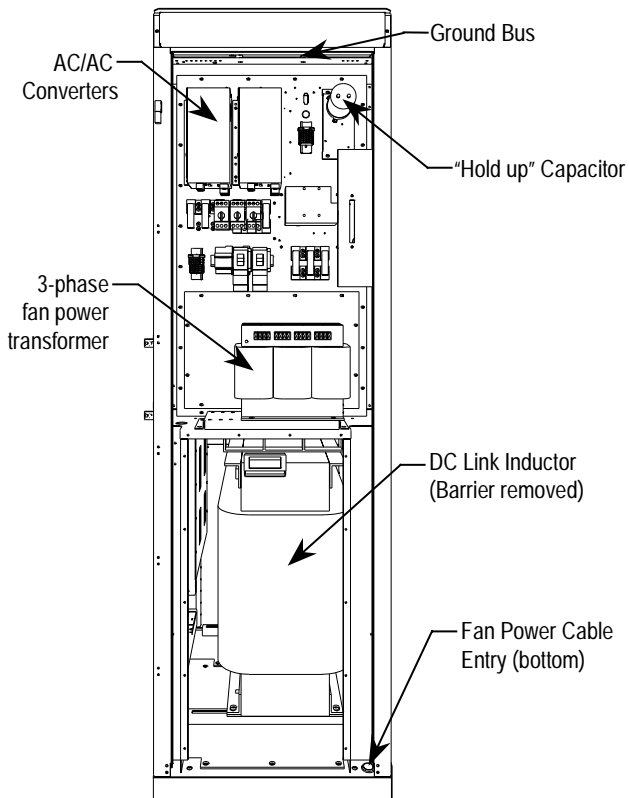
Baugruppen des Lüfterschaltsschranks mit Darstellung der Steuertafel
